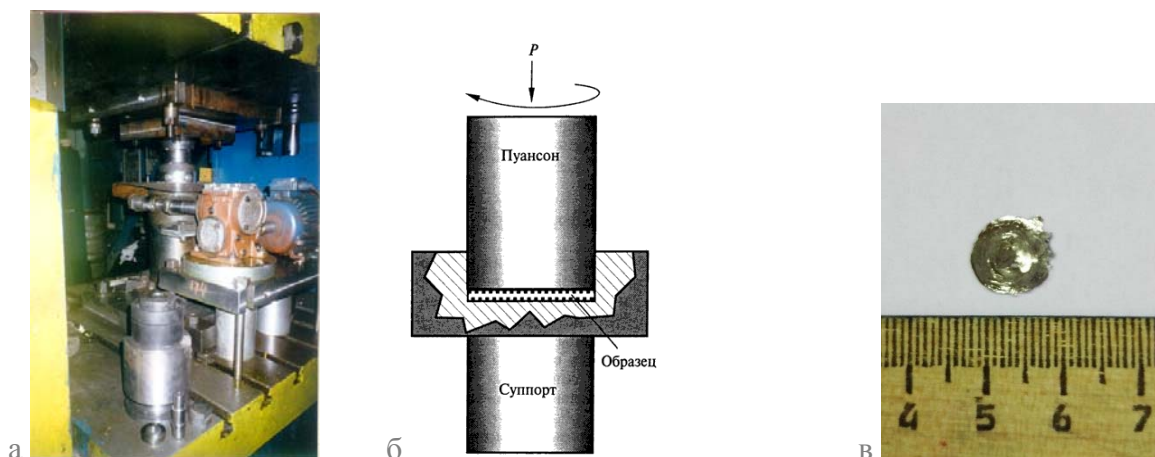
Внешний вид установки для интенсивной пластической деформации кручением (а), схема кручения под высоким давлением (б) и внешний вид образцов после интенсивной пластической деформации диаметром 10 мм.
